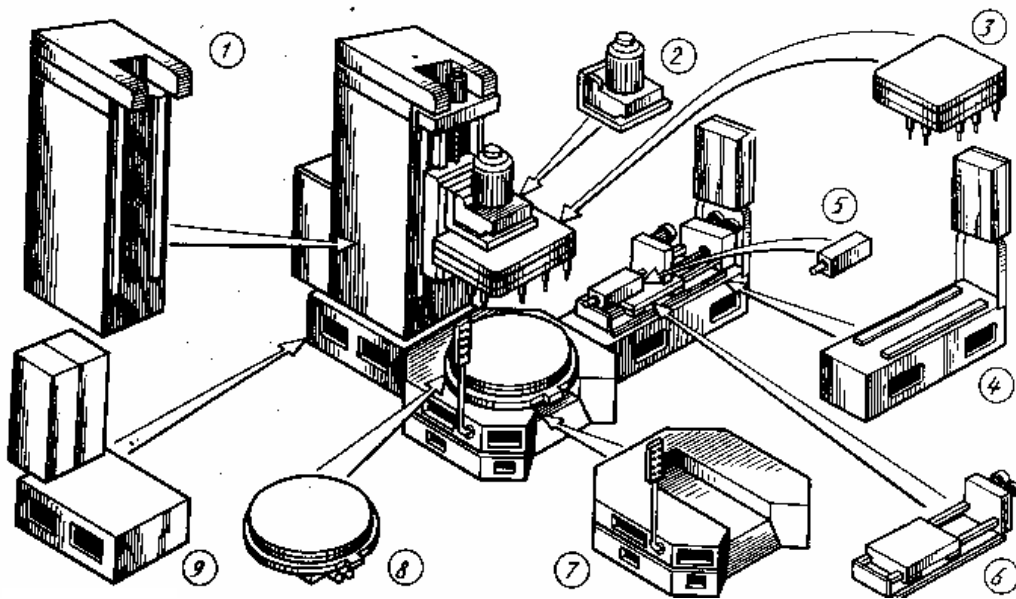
Варіант компонування агрегатного верстата: 1- стоек; 2 - силова бабка; 3 - багатошпindelна коробка; 4 - бокова станина; 5 - одношпindelна розточувальна бабка; 6 - самодіючий силовий стіл; 7 - центральна станина з пультом; 8 - поворотний ділительний стіл; 9 - станина - підставка
